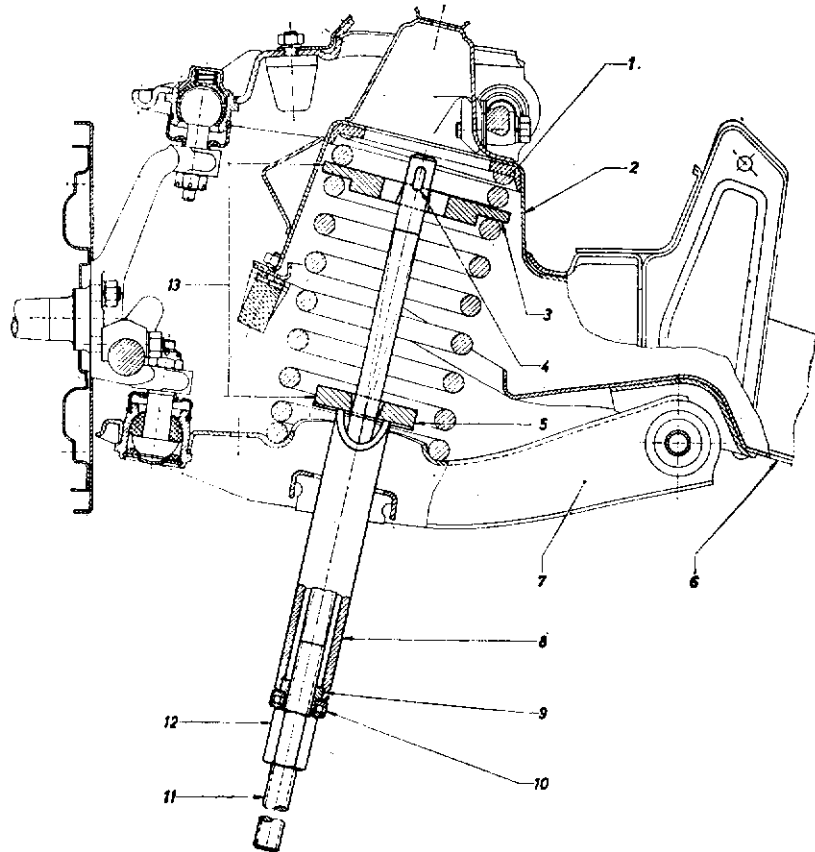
Compresseur de ressort en place - outils S 1034 et S 1158
